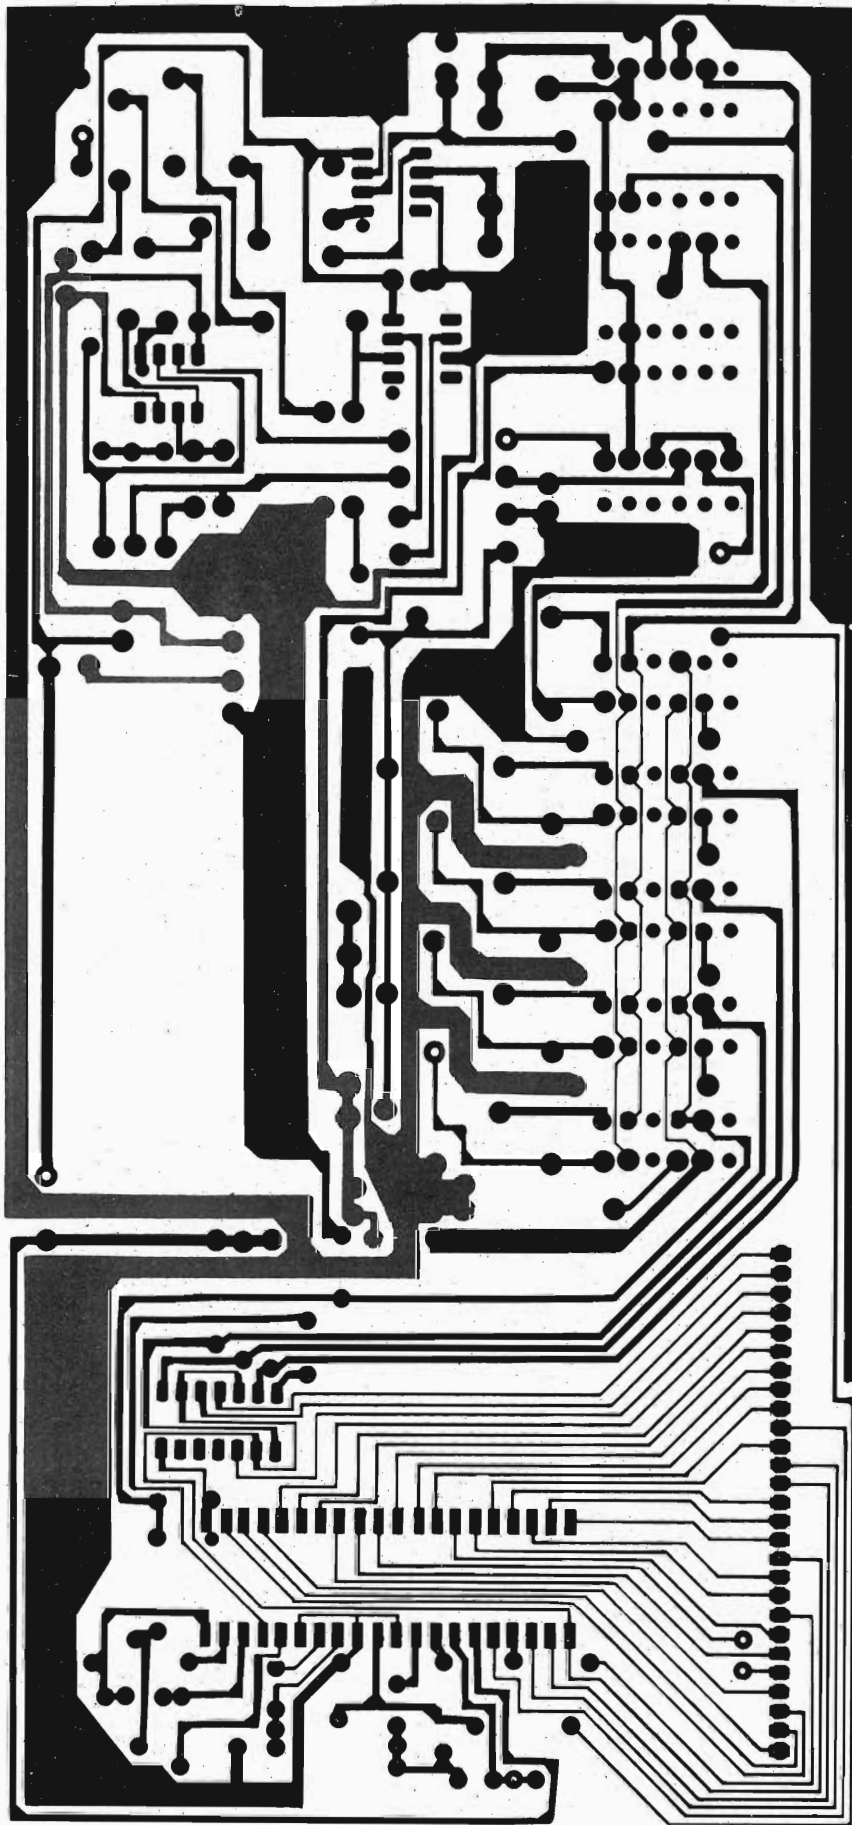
Circuito stampato della basetta visto dal lato rame in scala 1:1. Nell'eventuale realizzazione, porre particolare attenzione alla continuità delle piste più sottili.
